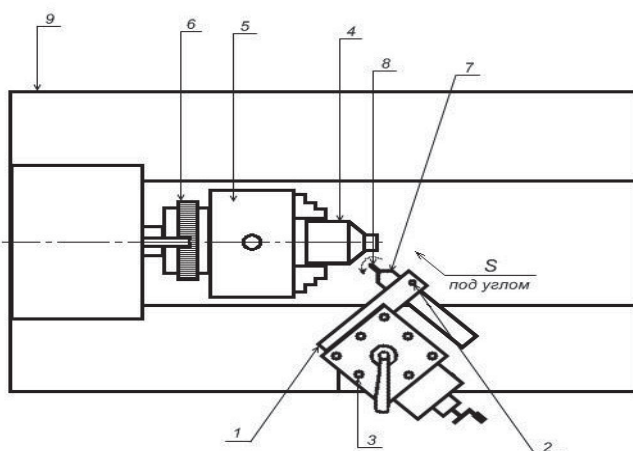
Схема универсального узла для обработки отверстий и пазов на конической поверхности детали
